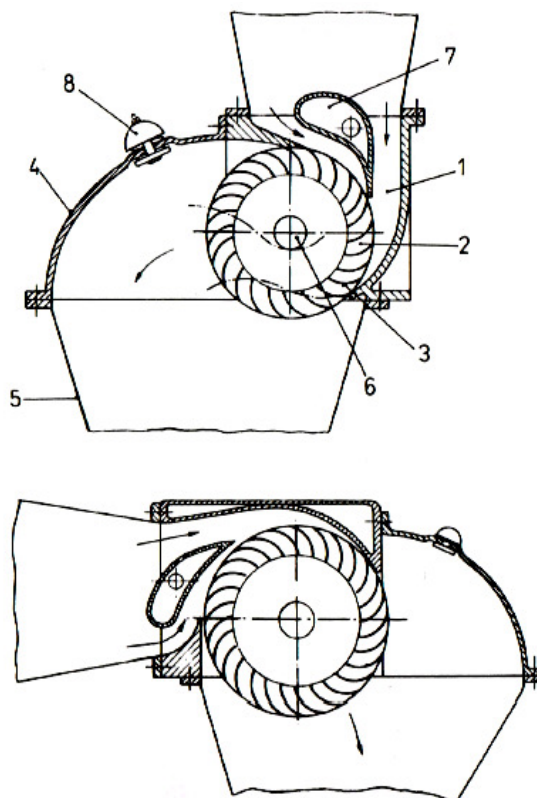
Proudění oběžným kolem Bánkiho turbíny [1]
